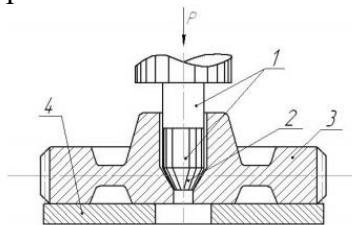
Схема прошивки отверстия ступицы зубчатого колеса на гидравлическом прессе: 1 – наставки; 2 – прошивень; 3 – зубчатое колесо; 4 – опора
